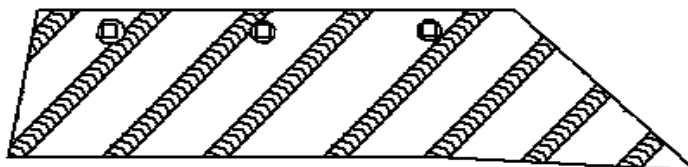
Схема наплавочного армирования (вариант, когда формирование валиков проводится по всей рабочей поверхности)
